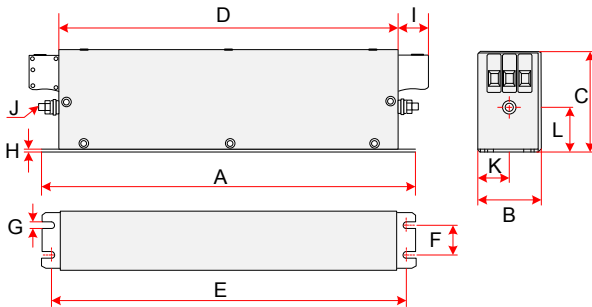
FN3258 系列 50-180A 滤波器尺寸图 (单位: mm)
